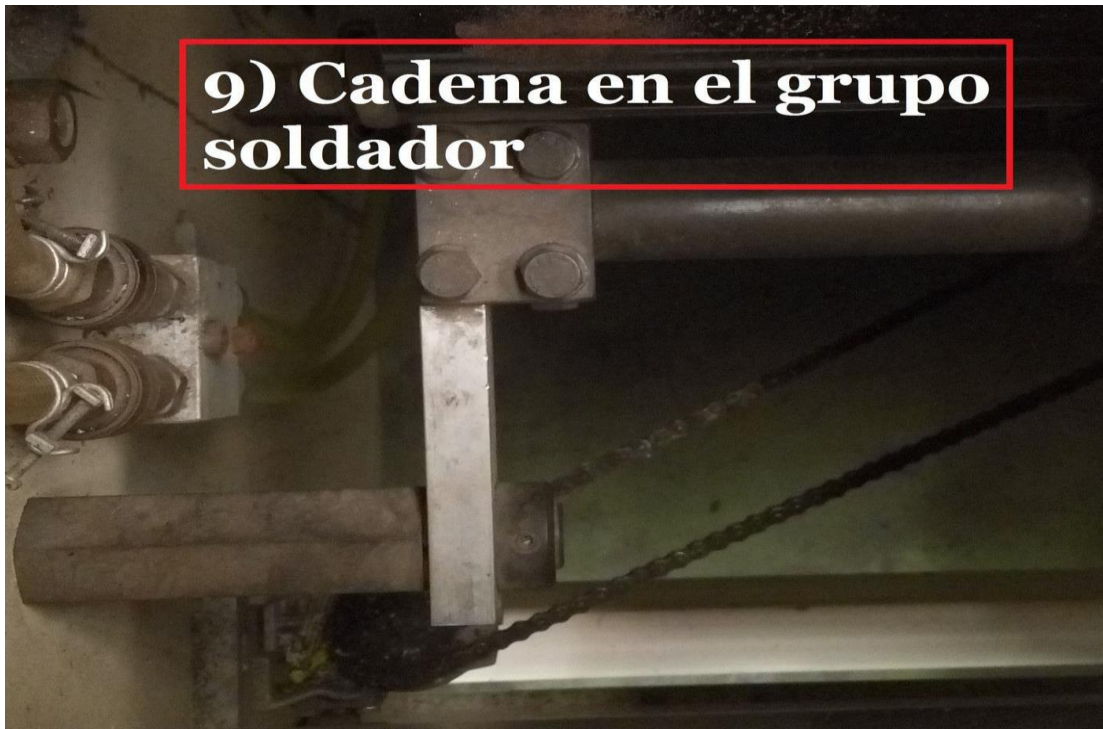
Piñón y cadena en el grupo soldador
